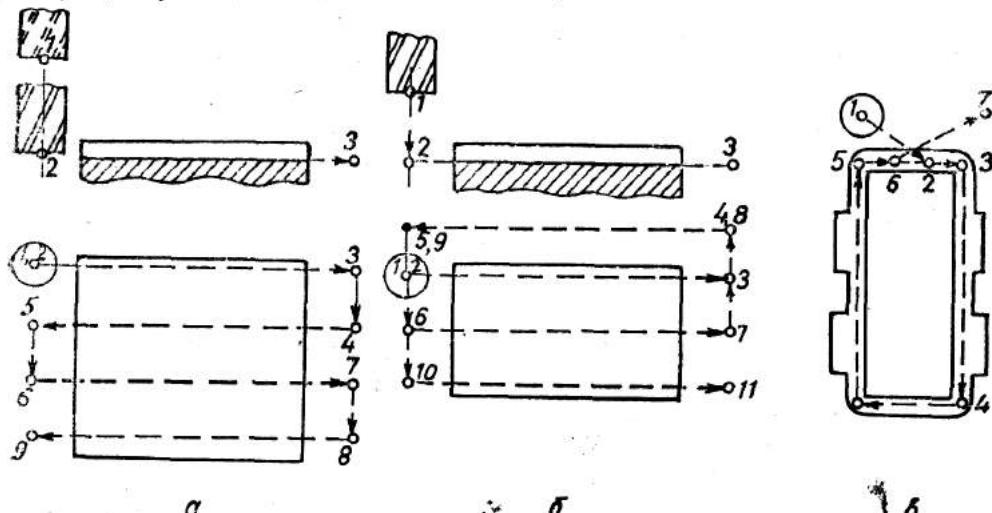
Схеми чорнового (а), чистового (б) і контурного (в) фрезерування площини торцевою фрезою.
